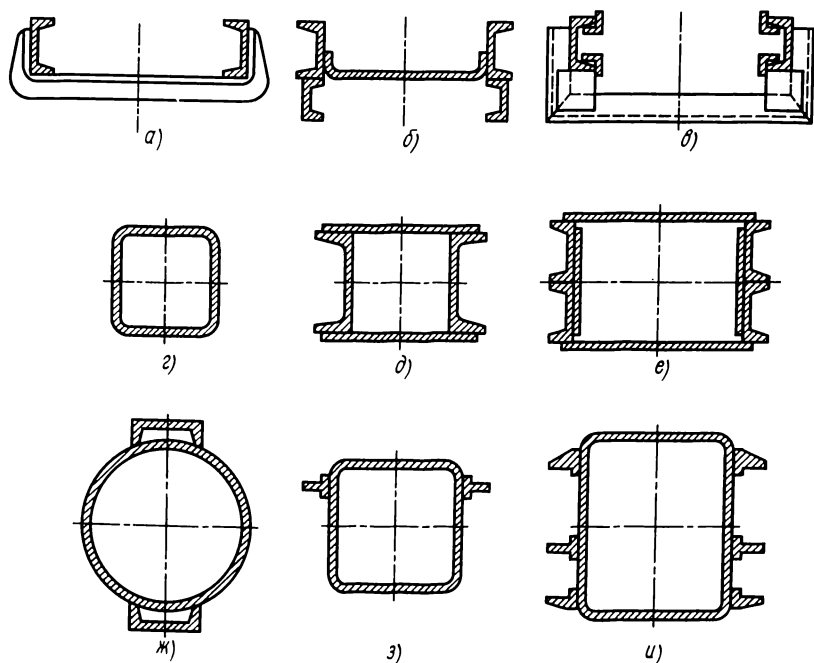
Сечения колонн мостовых кранов-штабелеров:
